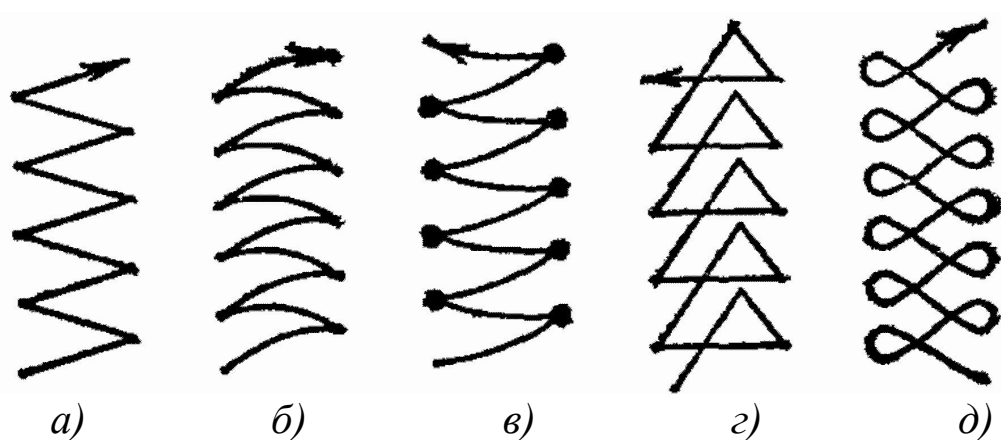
Траектории движения конца электрода: *a, б* – для равномерного прогрева сварочной ванны; *в, д* – для усиленного прогрева кромок; *з* – для усиленного прогрева корня шва
